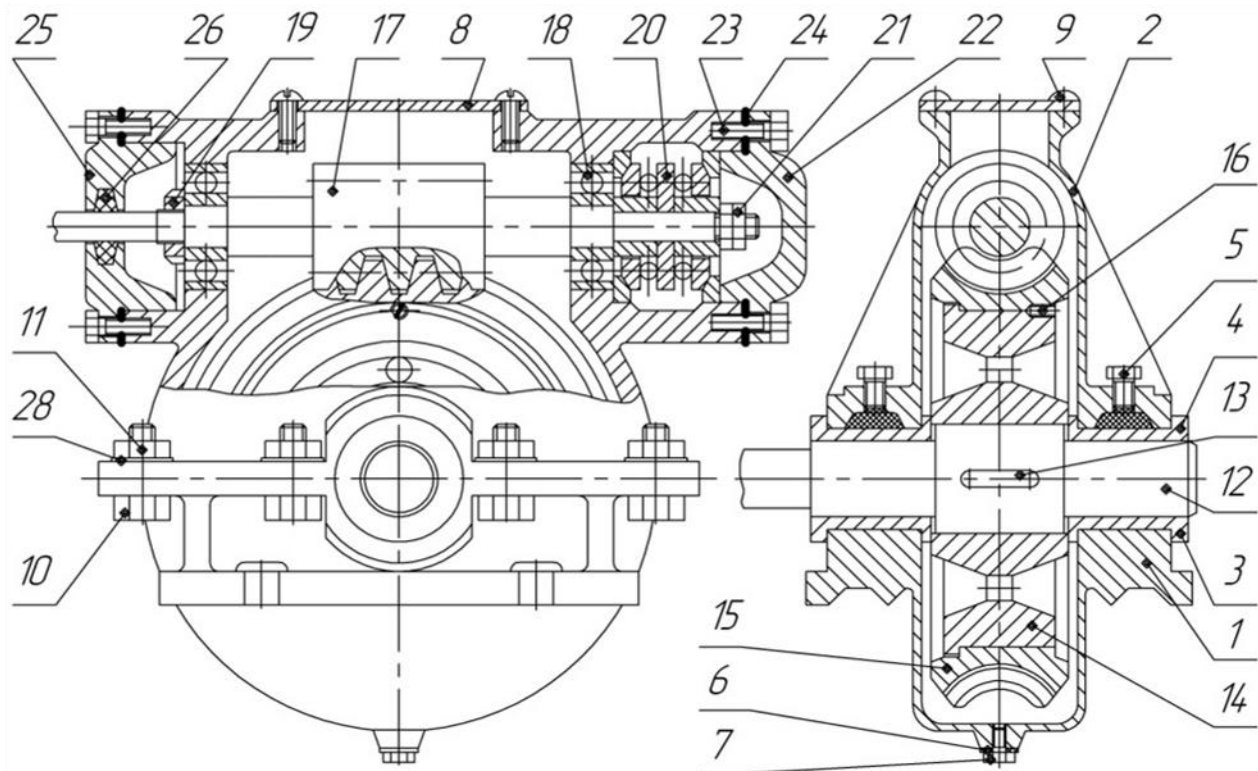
Складальні креслення черв'ячного редуктора P05.000 СК
